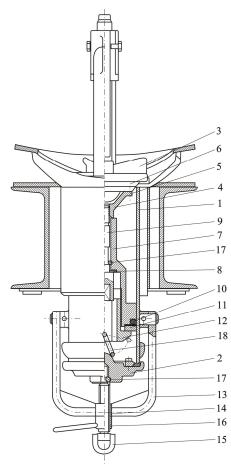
Конструкция сливного прибора с тройной защитой (разработка ОНИЛ «ТТОРЕПС»)
